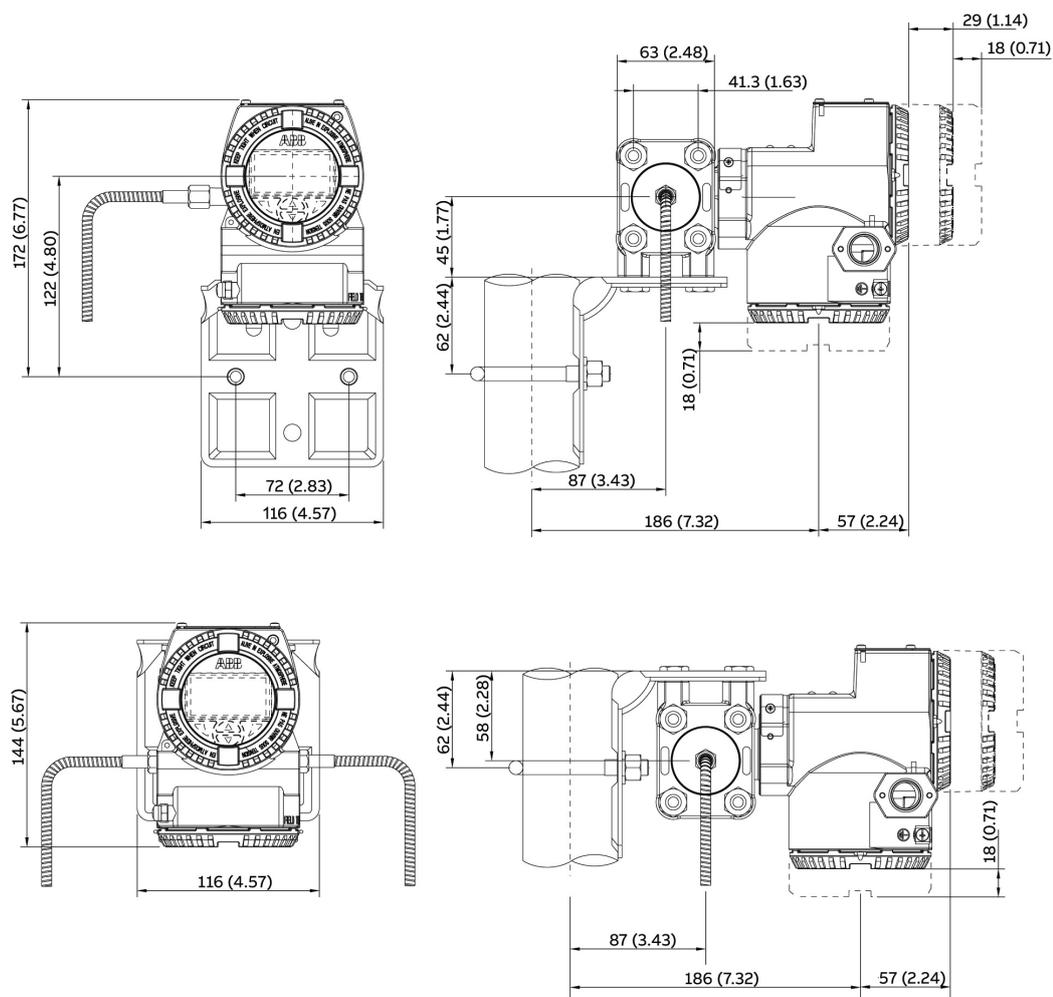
Montage sur tuyauterie - boîtier DIN
